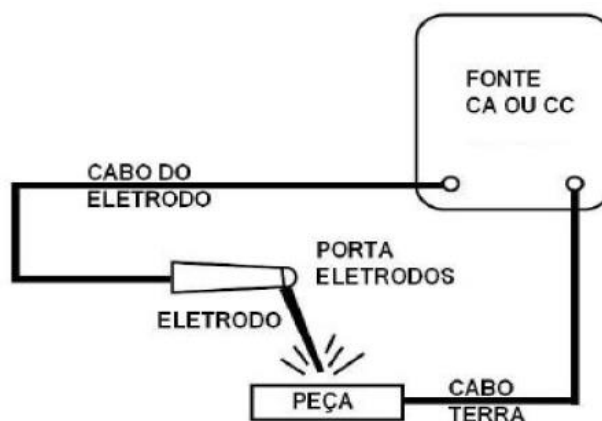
Circuito de soldagem por Eletrodo Revestido [13]
